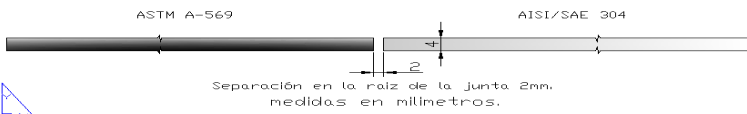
Conjunto de probetas de uniones disímiles de Acero Inoxidable Austenítico AISI/SAE 304 y ASTM A569, soldadas con un electrodo ER309L (vista lateral).
